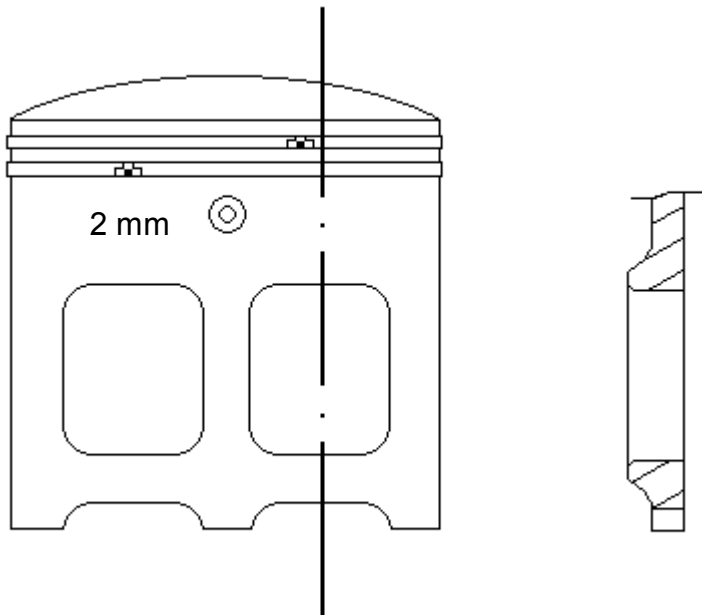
Kolbenbearbeitung auf der Einlaßseite (hintere Zylinder)
